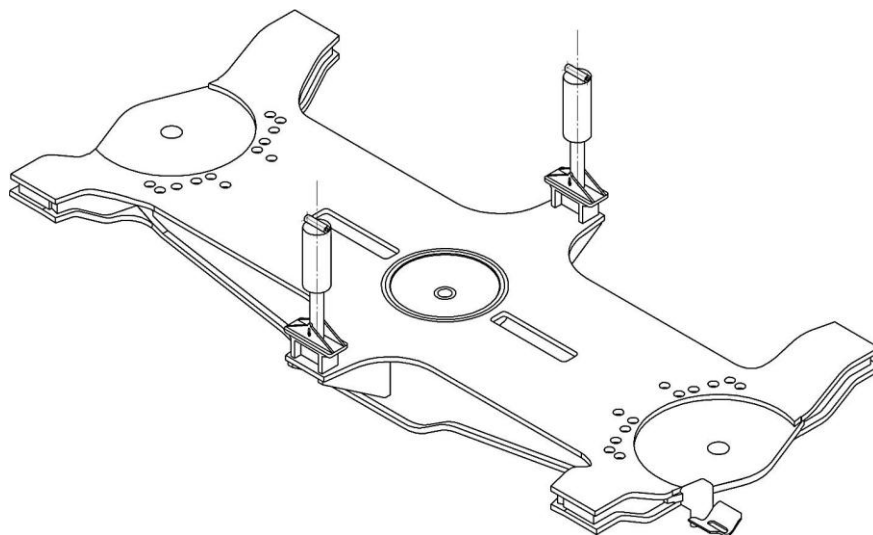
Первый вариант балансировочной системы с опиранием гидравлических упоров на скользяны соединительной балки
